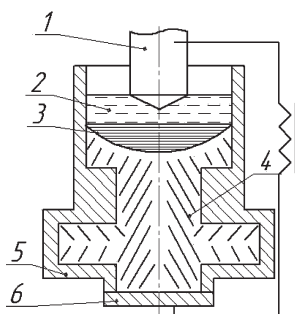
Схема ЭШЛ при выплавке в кристаллизаторе отливки целиком: 1 – электрод; 2 – шлаковая ванна; 3 – металлическая ванна; 4 – отливка; 5 – кристаллизатор; 6 – поддон
